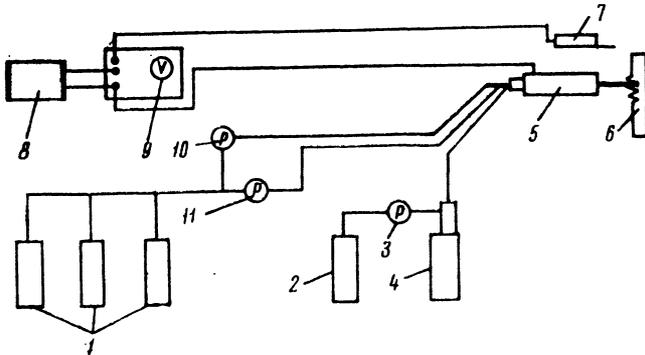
Схема бензино-кислородной резки (БУР): 1 — кислородный баллон; 2 — азотный баллон; 3 — редуктор азота; 4 — бензиновый баллон; 5 — резак; 6 — металл резки; 7 — зажималка; 8 — аккумулятор; 9 — вольтметр; 10 — редуктор режущего кислорода; 11 — редуктор подогревательного кислорода
